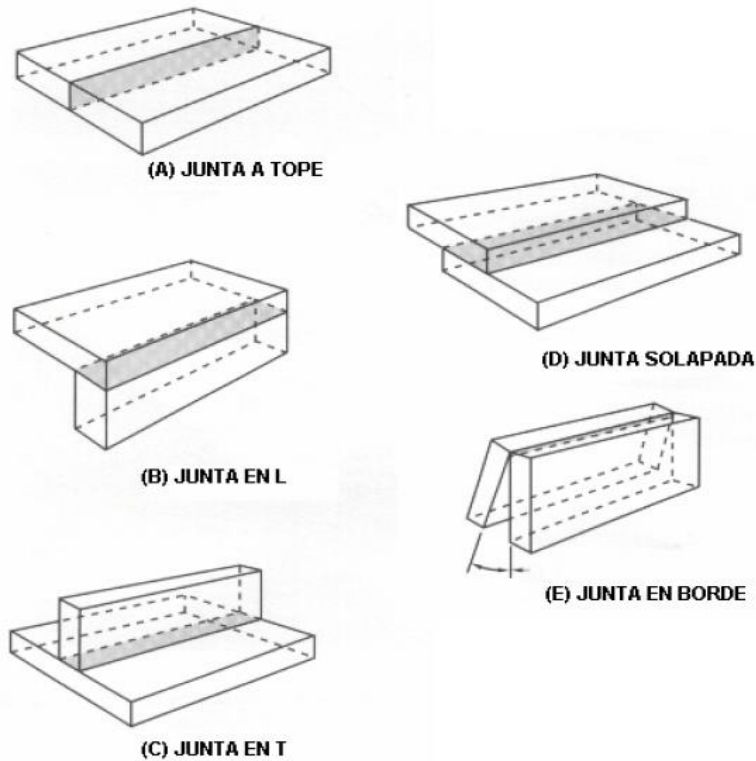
Juntas básicas, soldadura aplicable.
